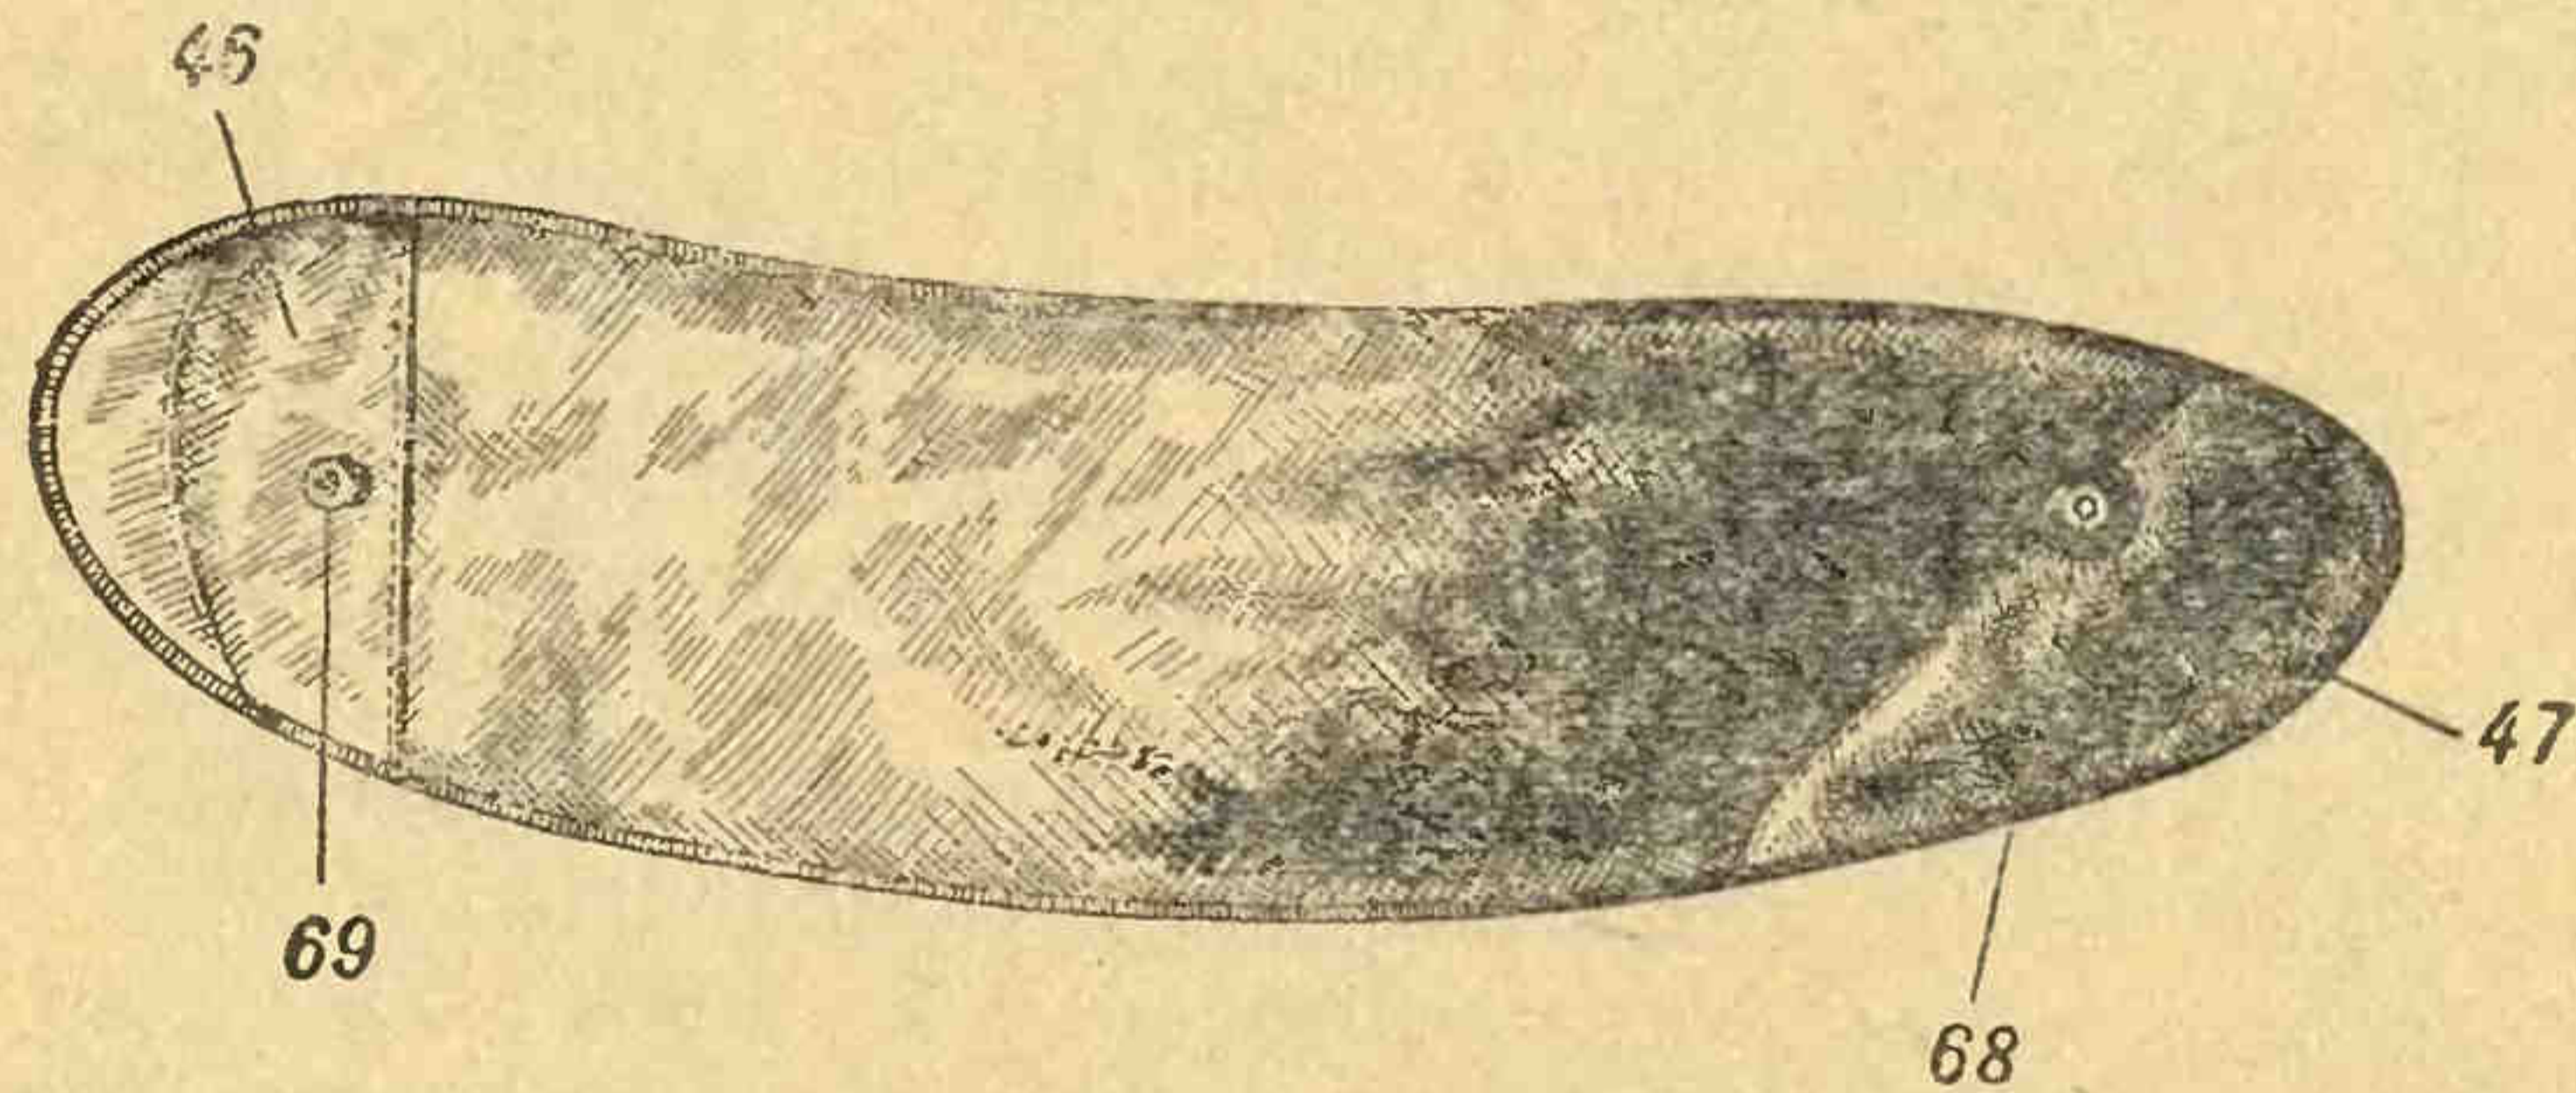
Подкладка под полки ленчика: 45 — передний козырек; 47 — задний козырек; 68 — матка задняя; 69 — матка передняя.
